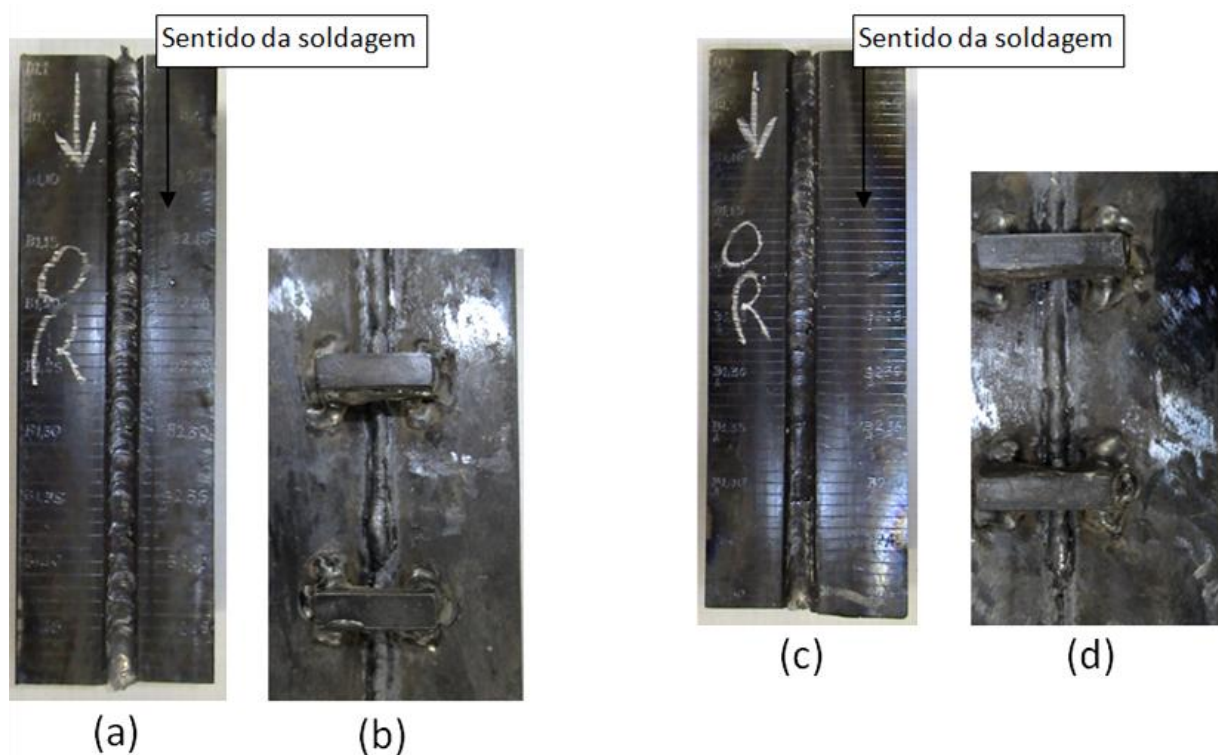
Soldagens que obtiveram sucesso nas regiões “sem e com defeito”.
